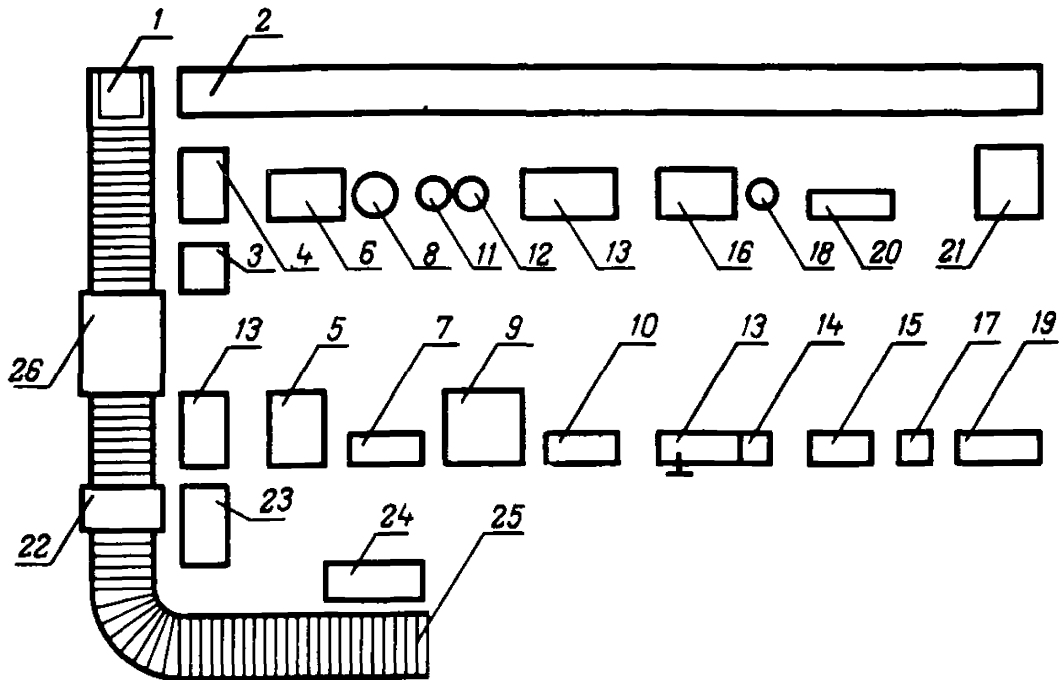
Типовая схема планировки рабочего места сборки двигателя:
